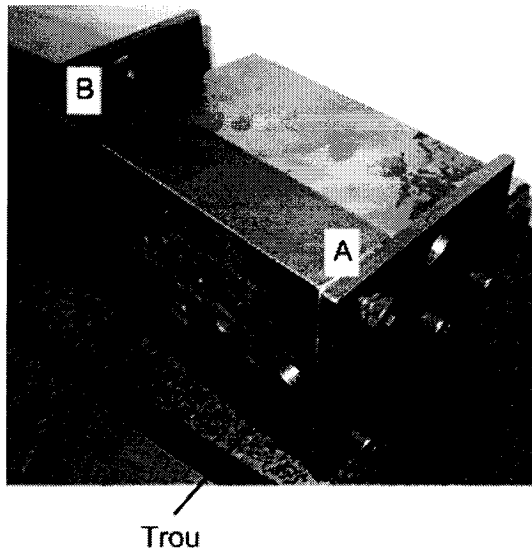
Trou permettant le bridage des deux pièces pendant la découpe
